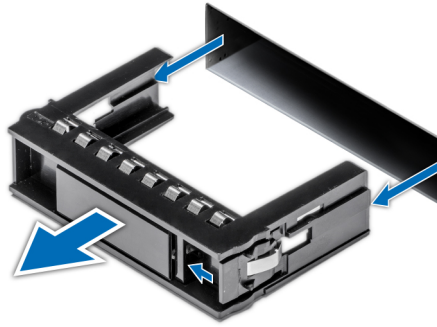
Entfernen eines Laufwerkplatzhalters
